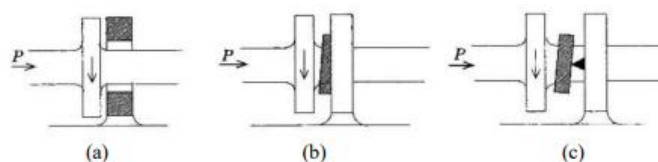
18 Sliderbearing, (a) thrust bearing (b) journal bearing
